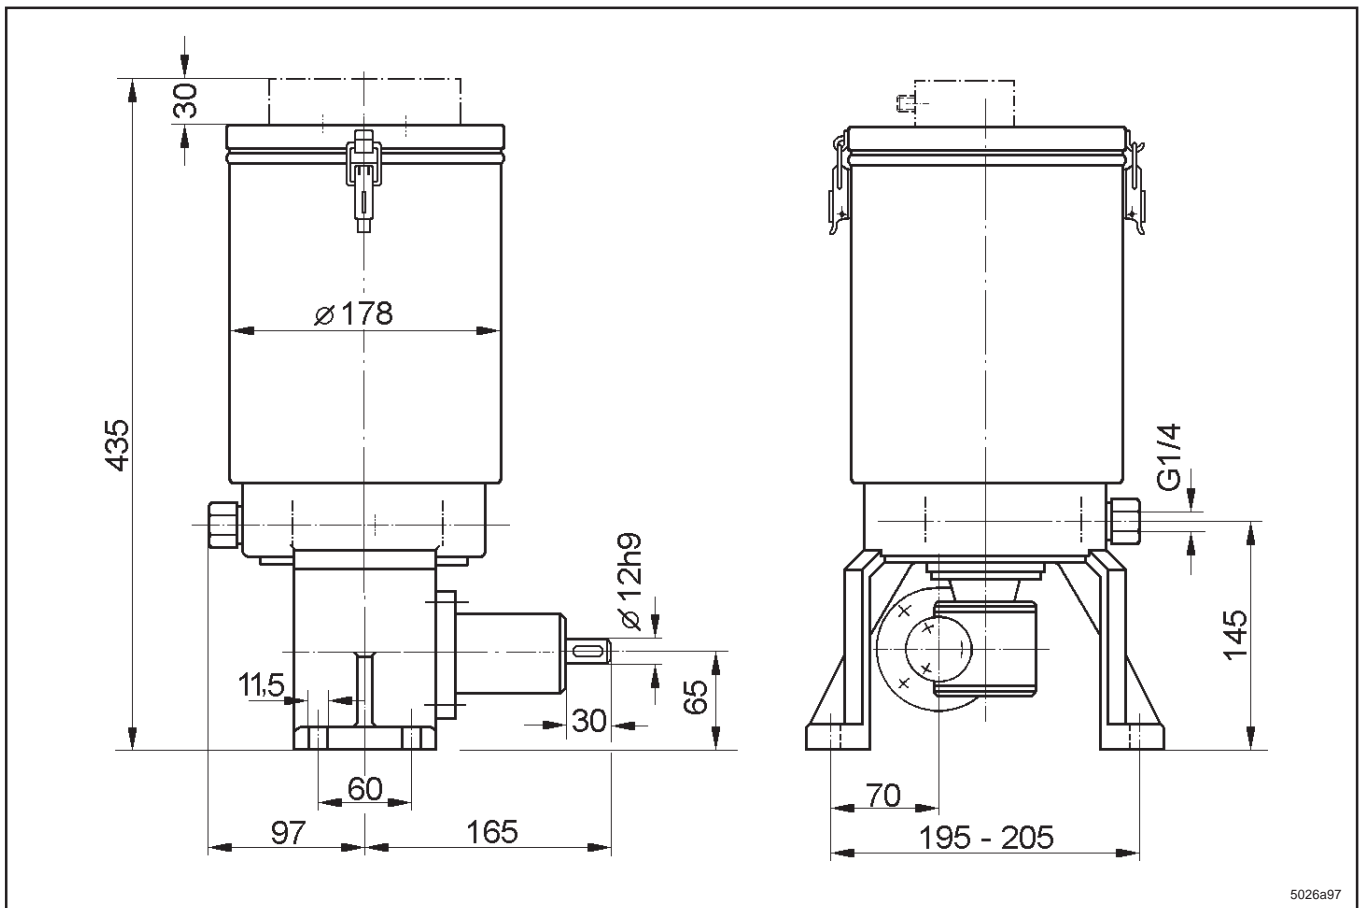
Maßzeichnung für Pumpe P 205, 1-stufiges Getriebe, 5l Blechbehälter, Motorantrieb
